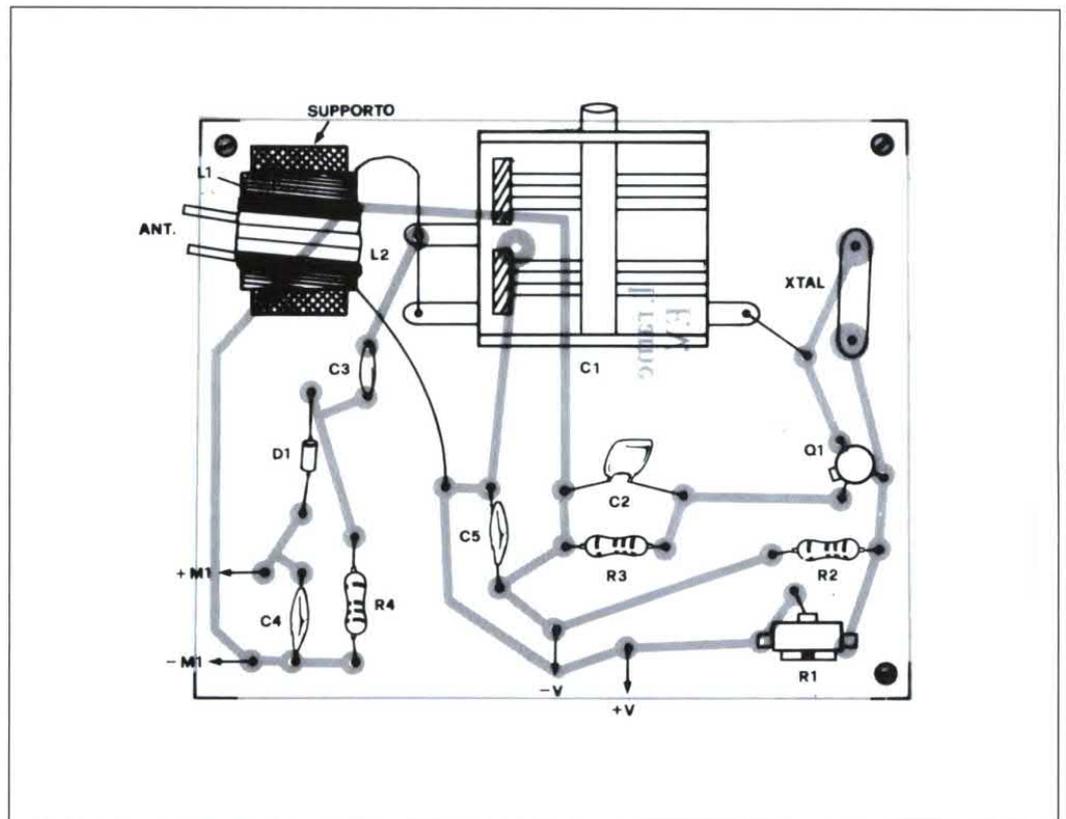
Piano di montaggio del trasmettitore per Onde Corte e CB.
